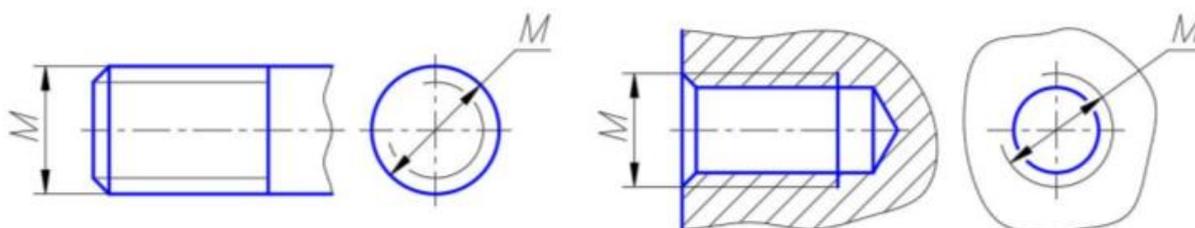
Примеры обозначения резьбы по наружному диаметру
